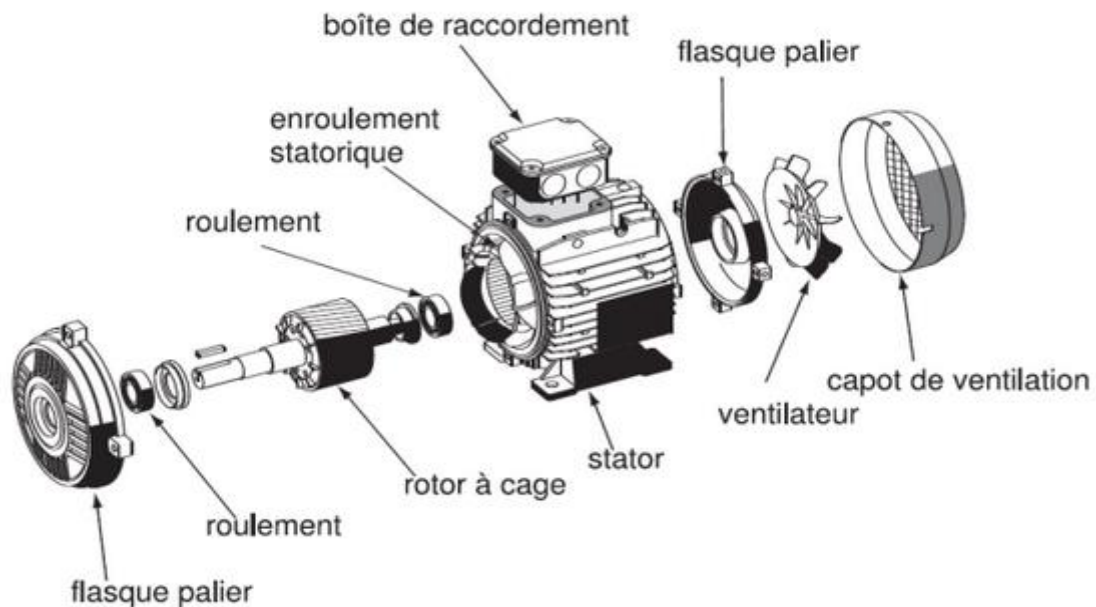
Vue éclatée d'une machine asynchrone à cage d'écureuil.
